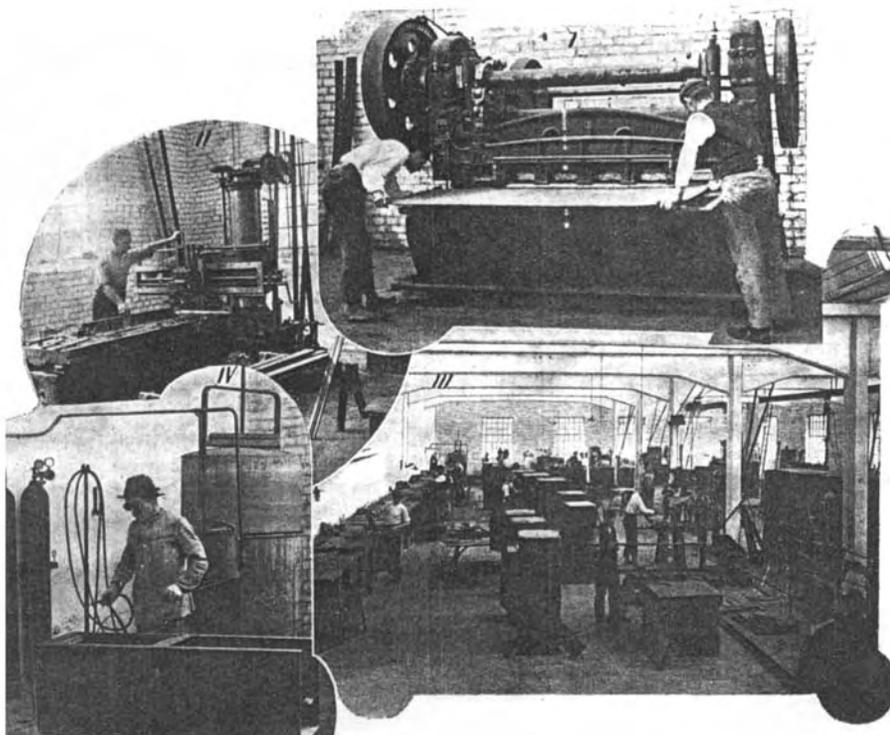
Vistas internas seção de cofres da Wallig. Na fotografia da direita logo acima vê-se a estrutura em concreto.
